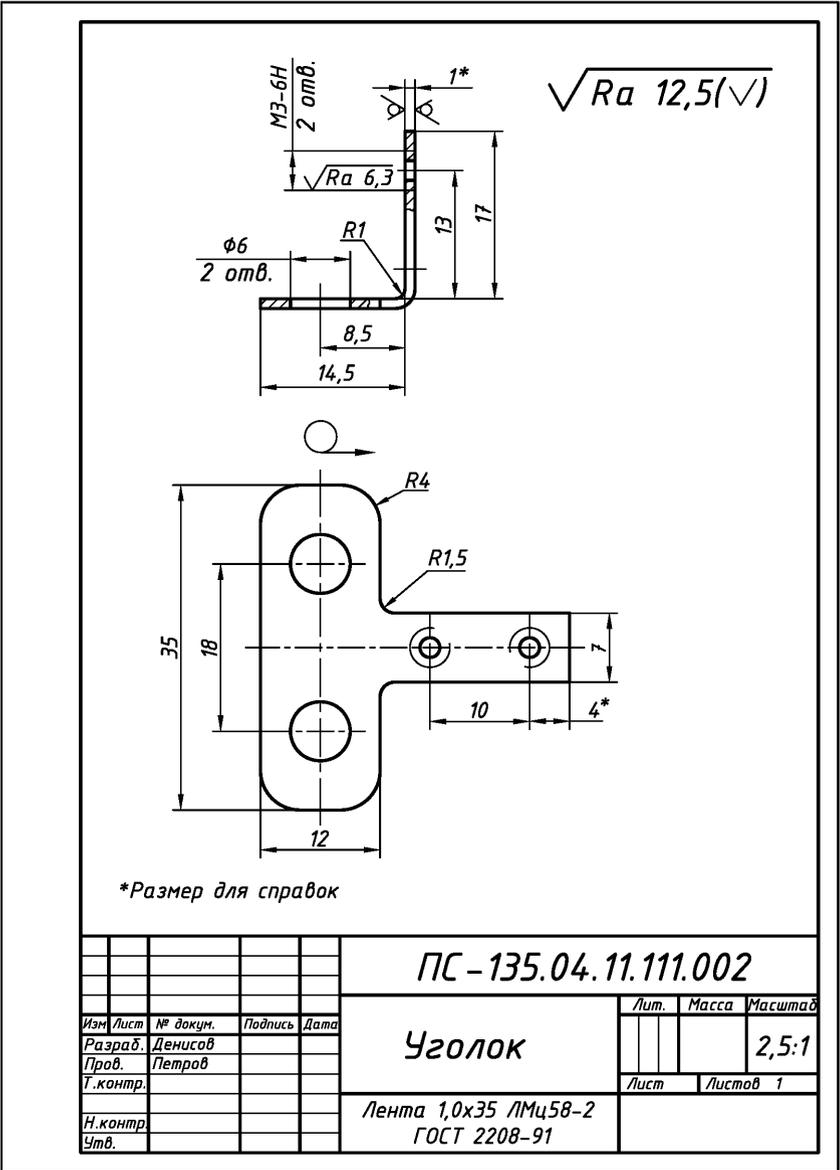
Оформление рабочего чертежа гнутой детали из тонколистового металла
